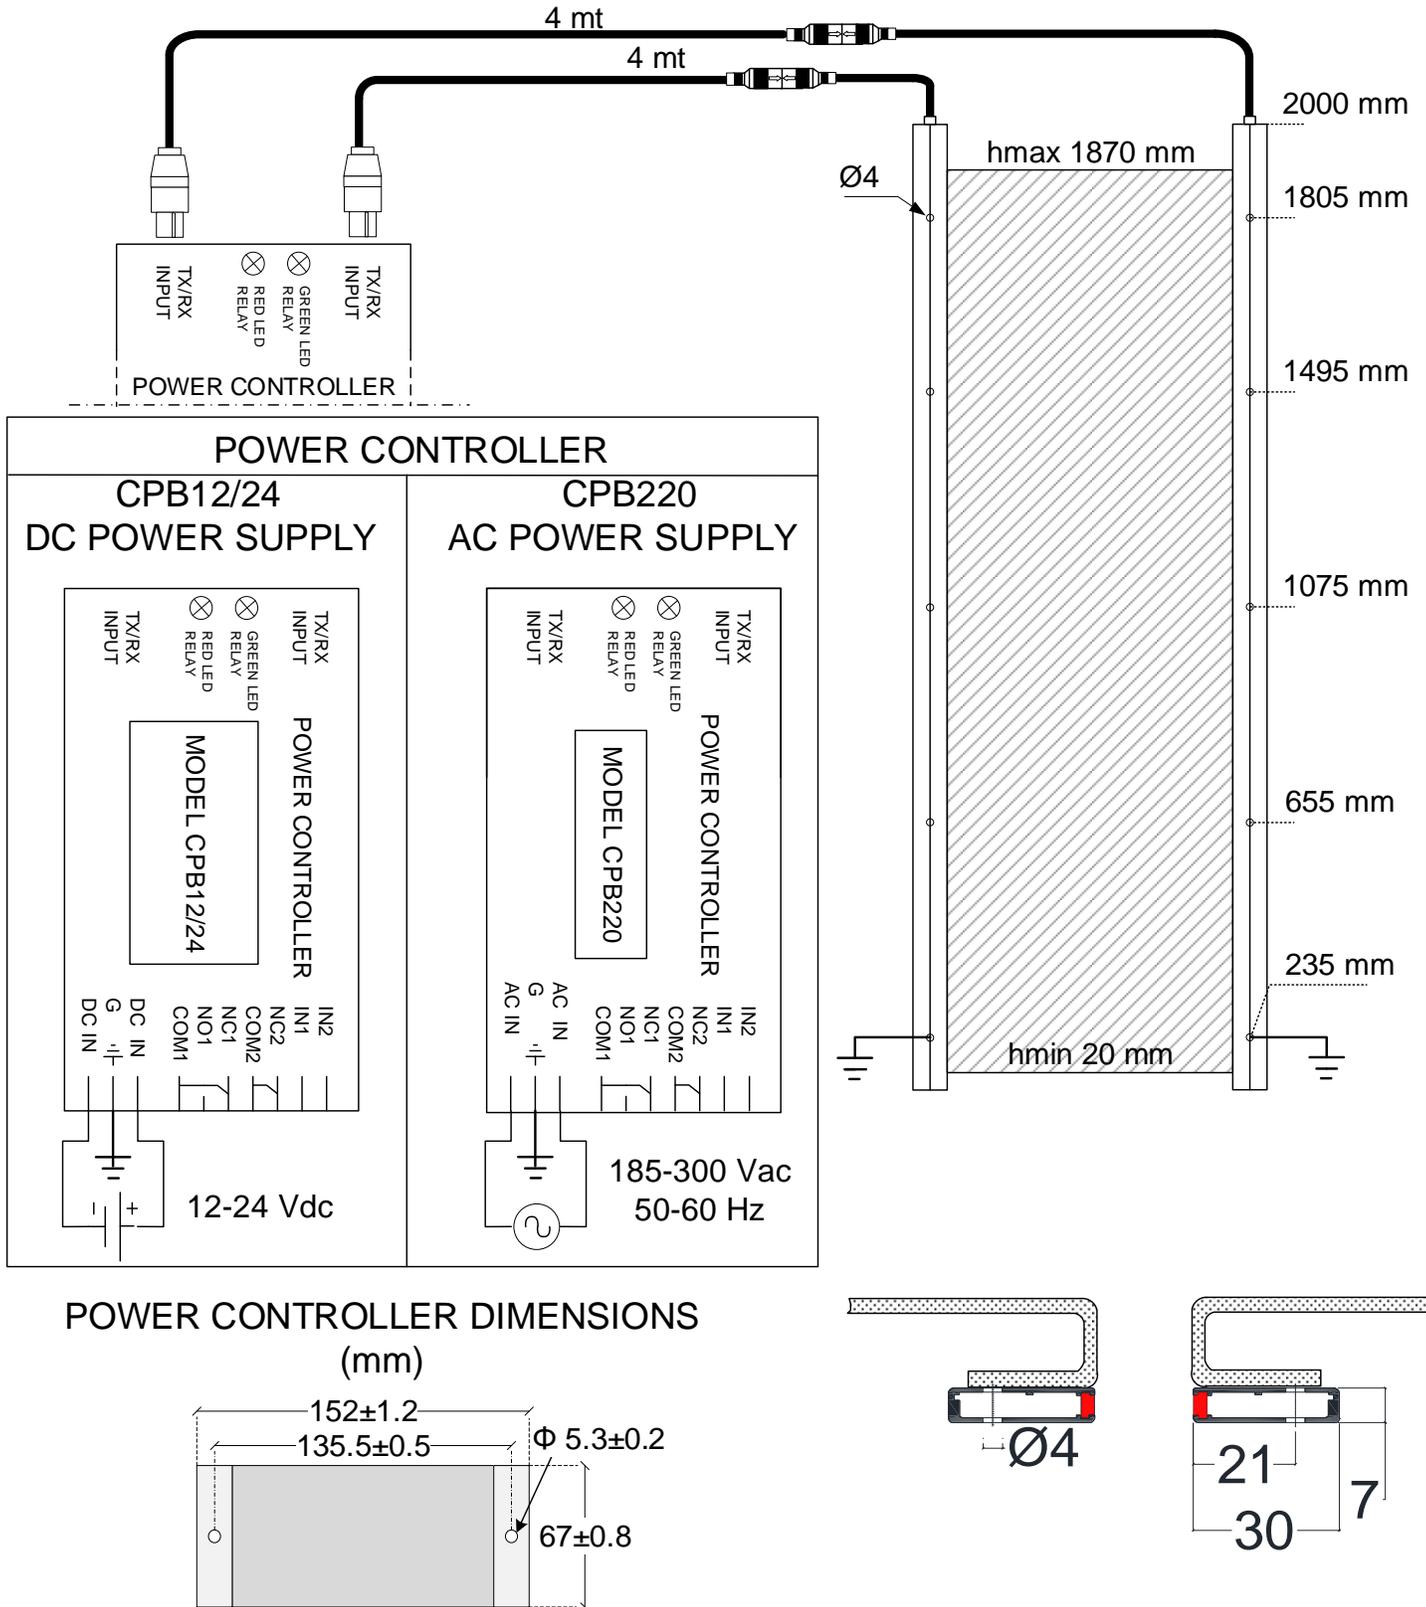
[IT] Montaggio e collegamento / [EN] Mounting and connection / [FR] Installation et branchement
